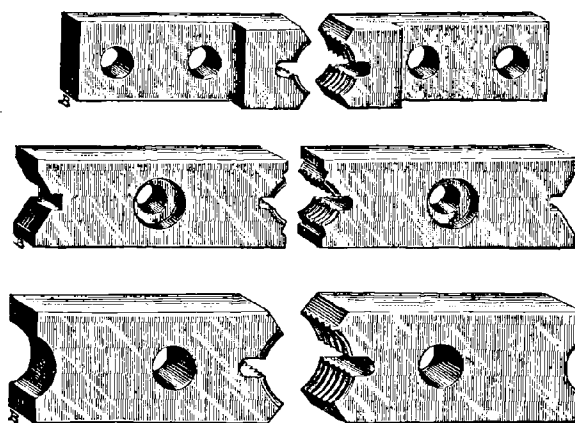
Coussinets en deux pièces pour machines à tarauder.
